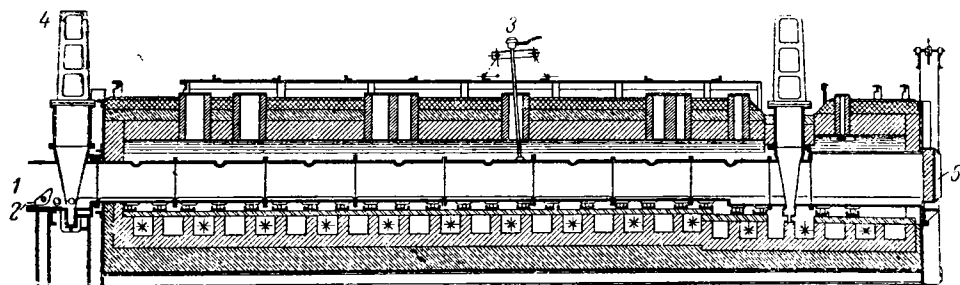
Печь для газовой цементации непрерывного действия с толкателем. 1 — загрузочное отверстие; 2 — толкатель для передвижения деталей в печи; 3 — подводка пиролизного газа в муфель печи; 4 — воздушный цилиндр с поршнем; 5 — загрузочное отверстие с заслонкой
